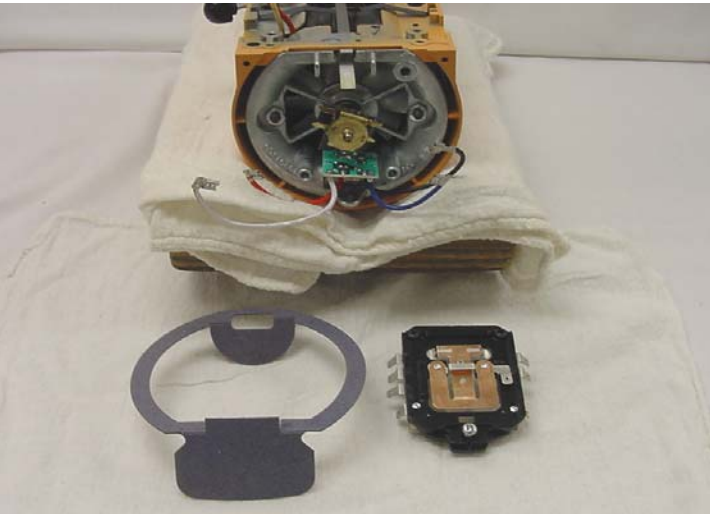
Motorgehäuse nach Entfernen der hinteren Dichtung/Abdeckung und der Steuerplatte.
